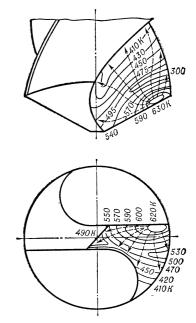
Температурное поле на поверхностях сверла (деталь — сталь 45; сверло из быстрорежущей стали; v=25~м/мин; s=0,11~мм/об; без охлаждения).
